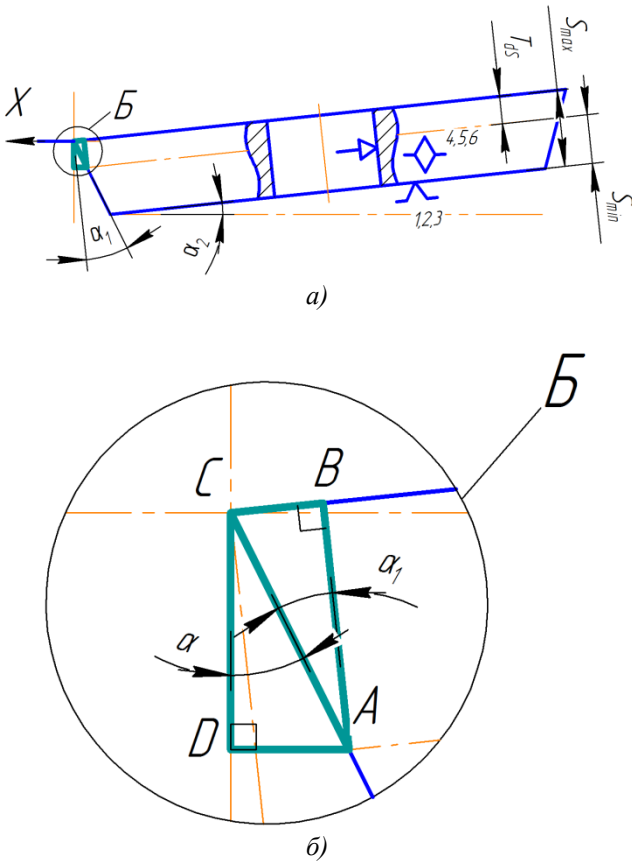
Схема для определения влияния допуска толщины пластины S на настроечный размер: а – общий вид; б – вершина резца
